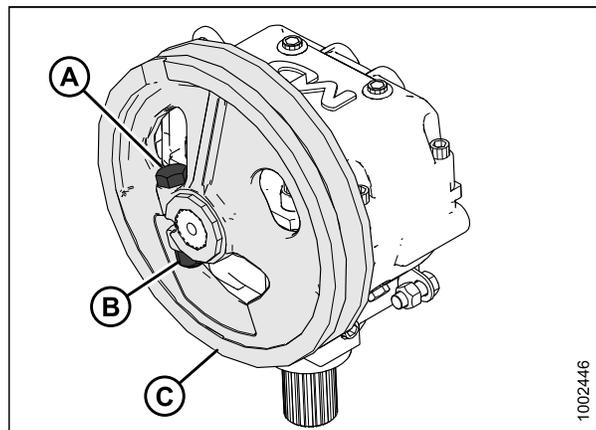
Редуктор привода ножа (МКШ) и шкив
